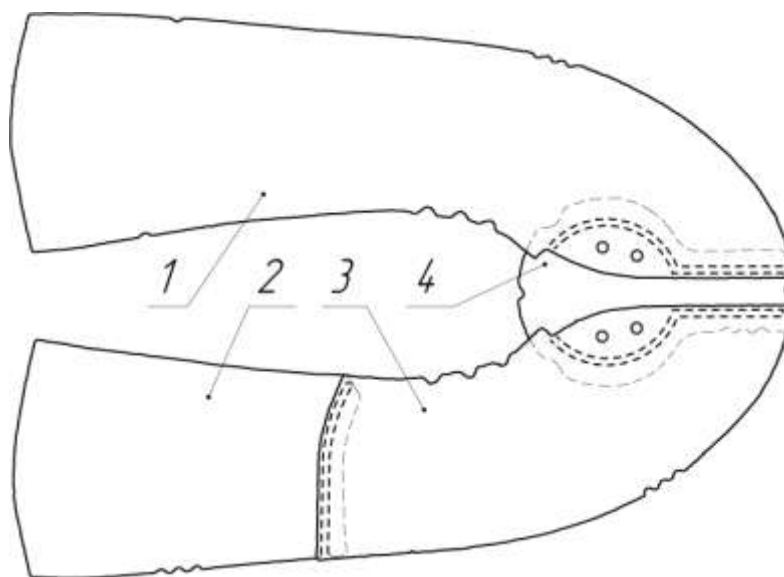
Схема заготовки верха туфель дошкольных для девочки
